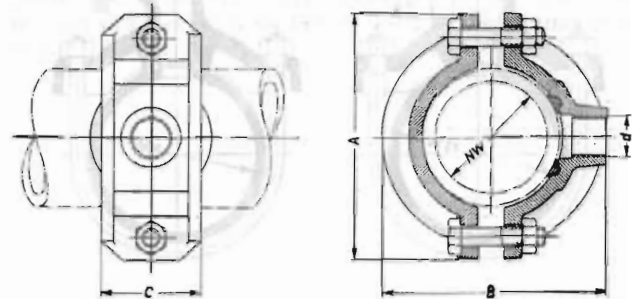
Ventil-Anbohrbrücke für seitliche Anbohrung mit Gewindeabgang für Asbestzement-Röhre
